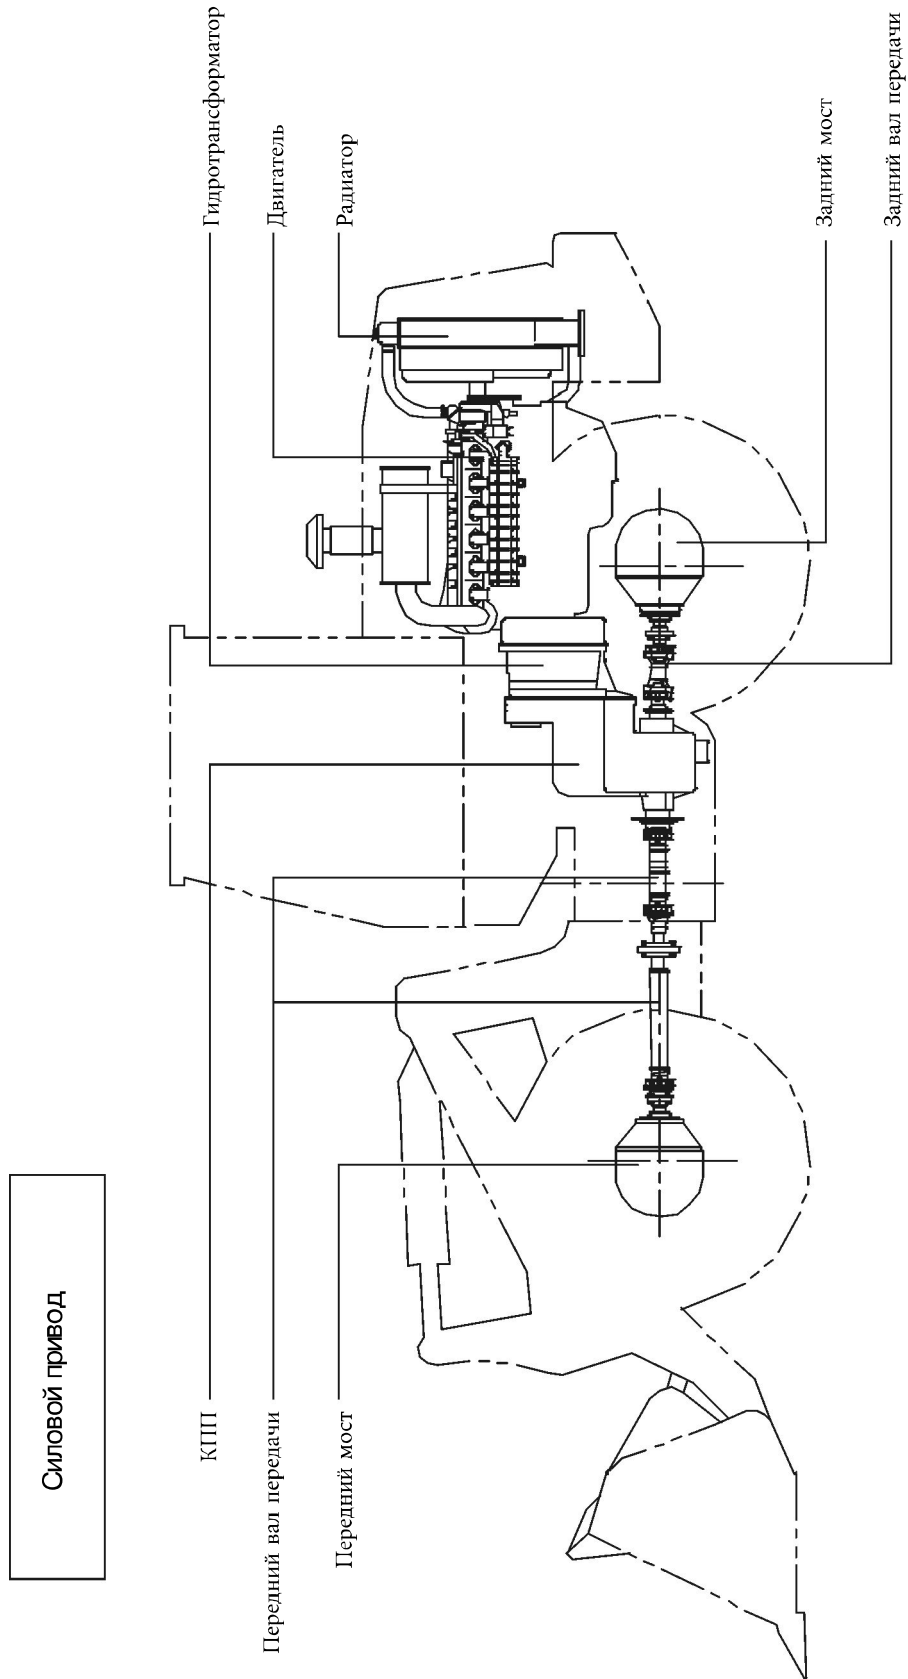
动力传动装置外形图和部件名称示意图 图 1-2 Внешний вид силового привода, наименование частей и деталей и их схемы
